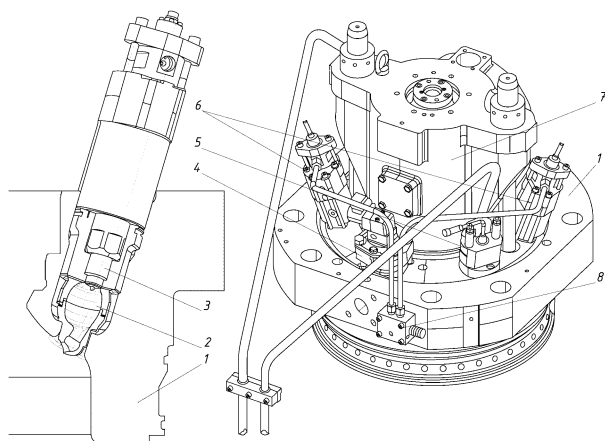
Модуль запального зажигания газозадушенной смеси газодизельного двигателя RT-flexDF и его установка на крышке цилиндра: 1 – крышка цилиндра; 2 – вихрекамера; 3 – форсунка подачи запального топлива; 4 – воздушный клапан; 5 – форсунка подачи резервного жидкого топлива; 6 – запальный модуль; 7 – корпус выпускного клапана; 8 – коллектор подвода запального топлива
